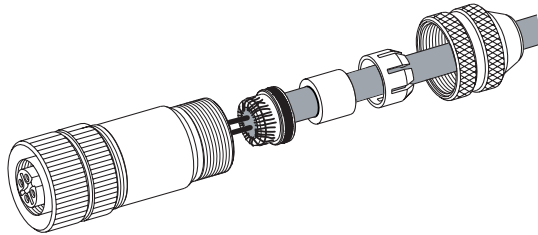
Montage Buchse/Stecker und Kabel
